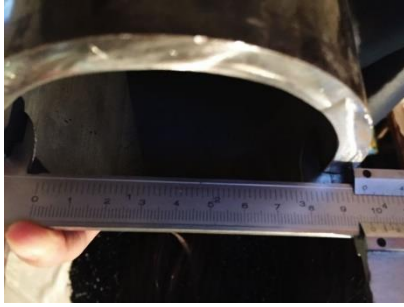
Exceso de sobre espesor (soldadura a tope) en la probeta número 3
